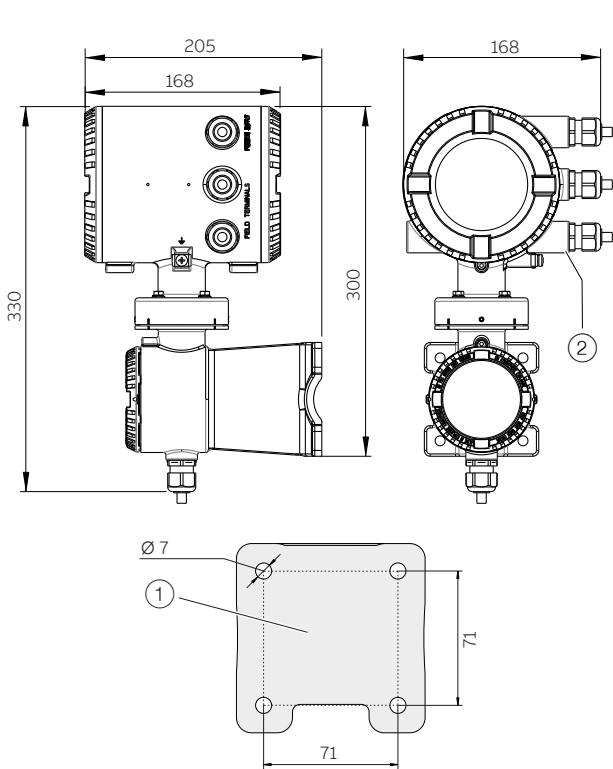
Montageabmessungen Zweikammer-Gehäuse
